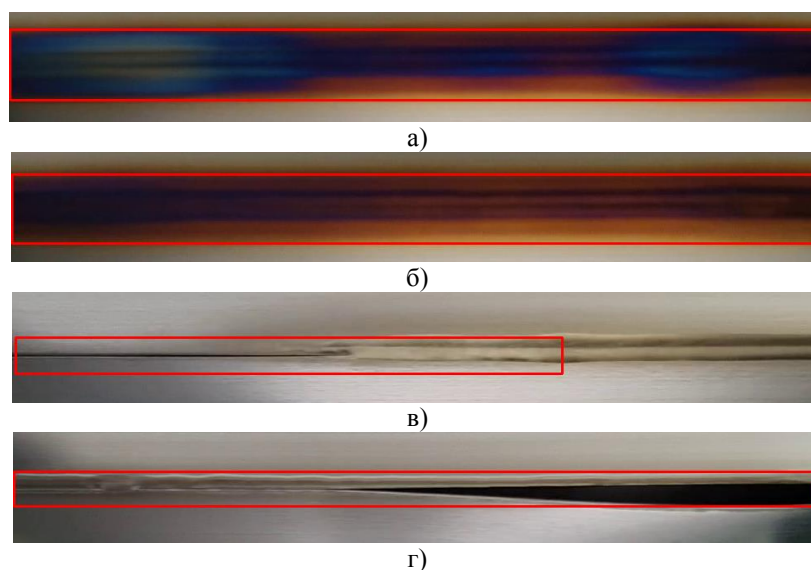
Примеры локализации дефектов сварки на кадрах видеопотока: окисление металла (а), (б); несплавление металла (в), (г)
